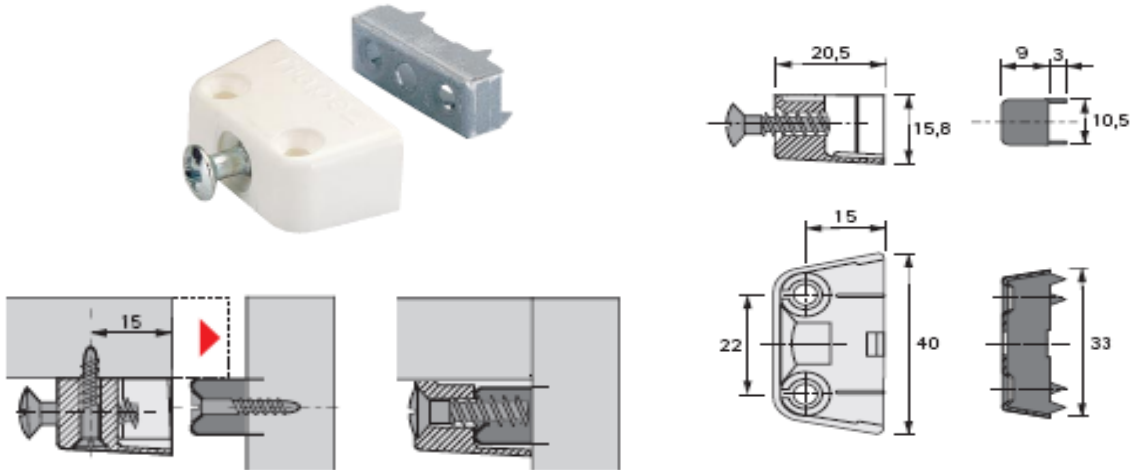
Eksantrik bağlantı elemanı (blum) (ölçüler mm) (19).
